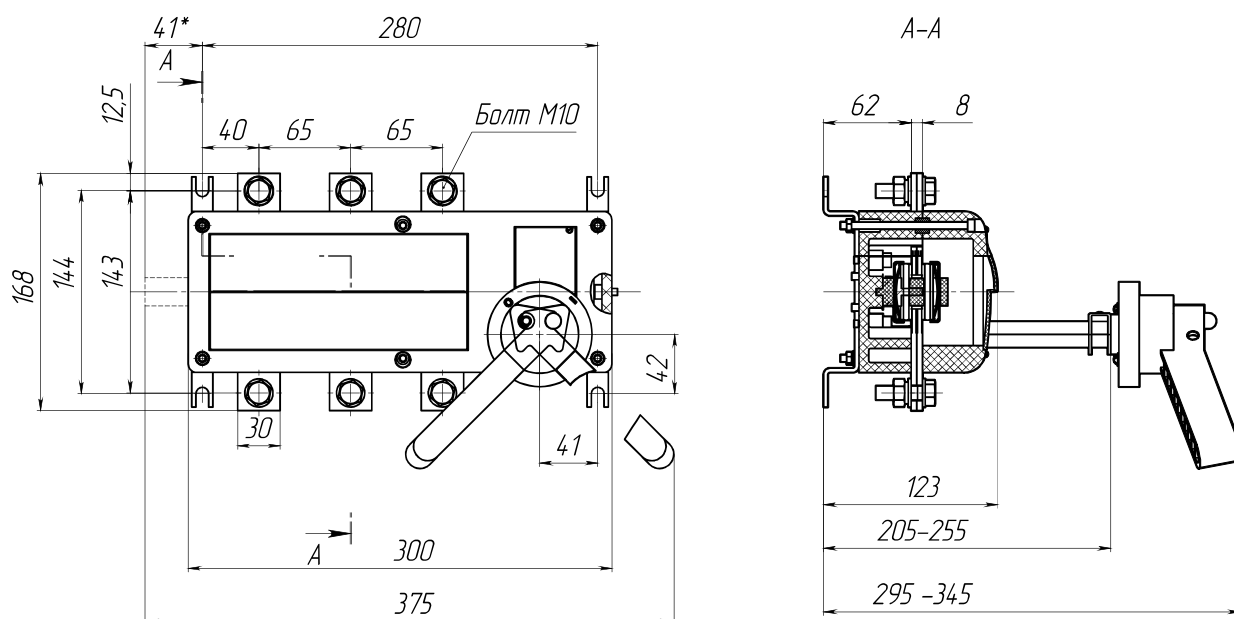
Выключатель-разъединитель ВНК-37-31130-32 УХЛ3
